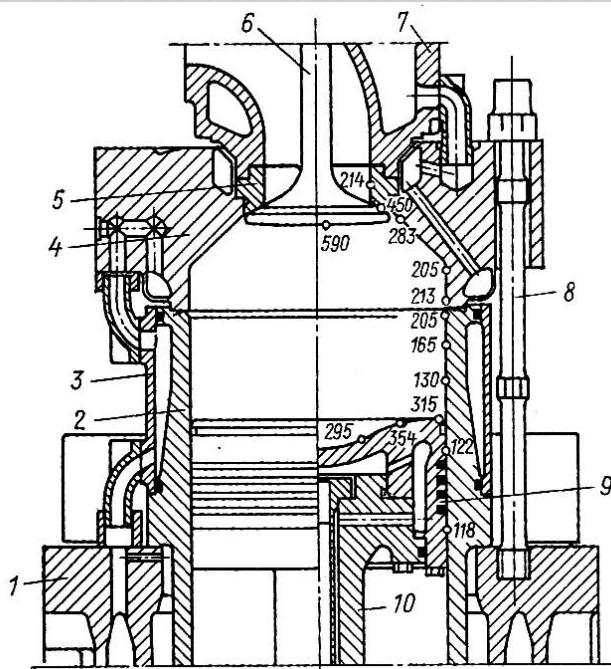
Циліндропоршнева група дизеля L35MC:
